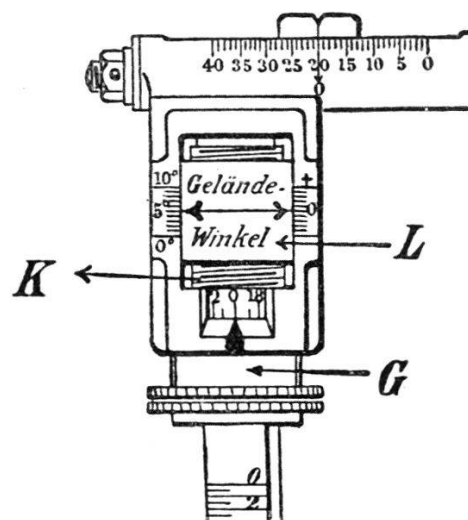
Hausse-niveau, tête hausse, vue de derrière.
